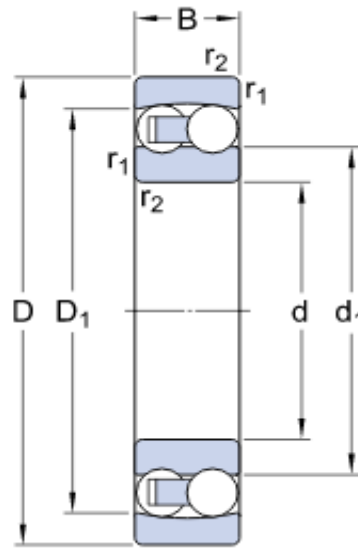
18: Dimensiones del rodamiento 1200 [17]
